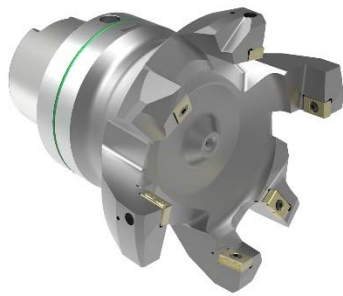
Überdrehwerkzeug mit Tangentialtechnologie
